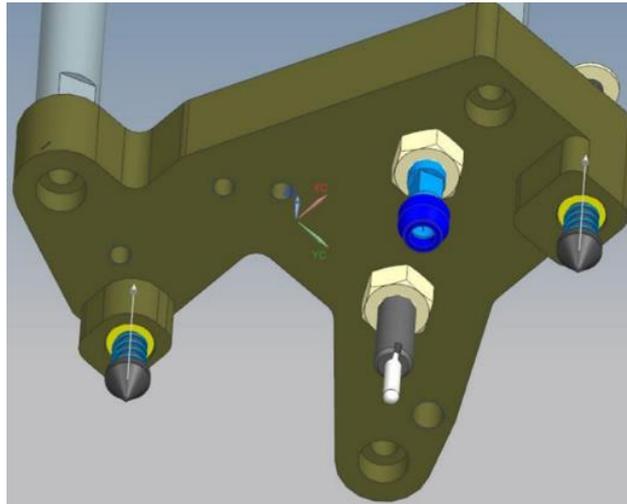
3D CAD-модель центруючого вузла лівої частини центральної головки
